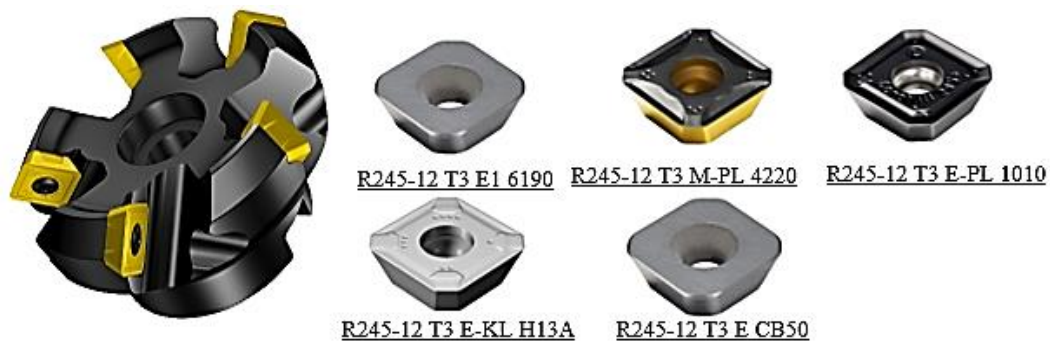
Торцева фреза R245-100Q32-12M для обробки чавунів компанії Sandvik Coromant
